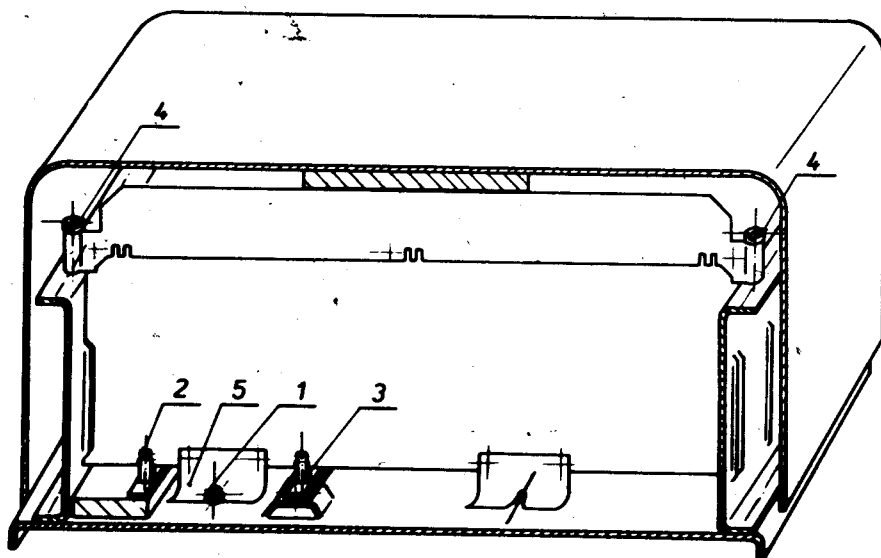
Otočené uspořádání rozvodnice se zesilovací soupravou
